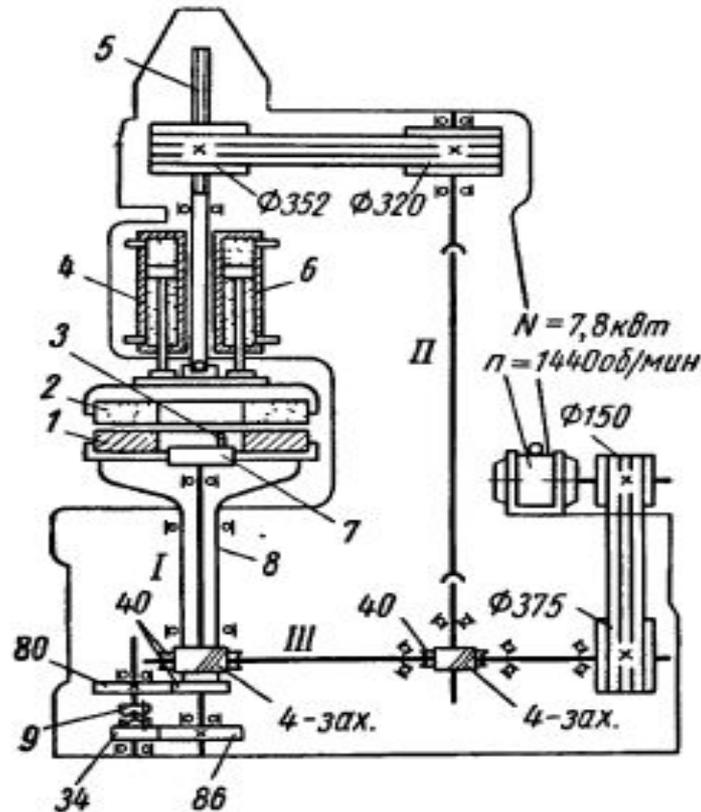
Кинематическая схема притирочного станка мод. 3816
